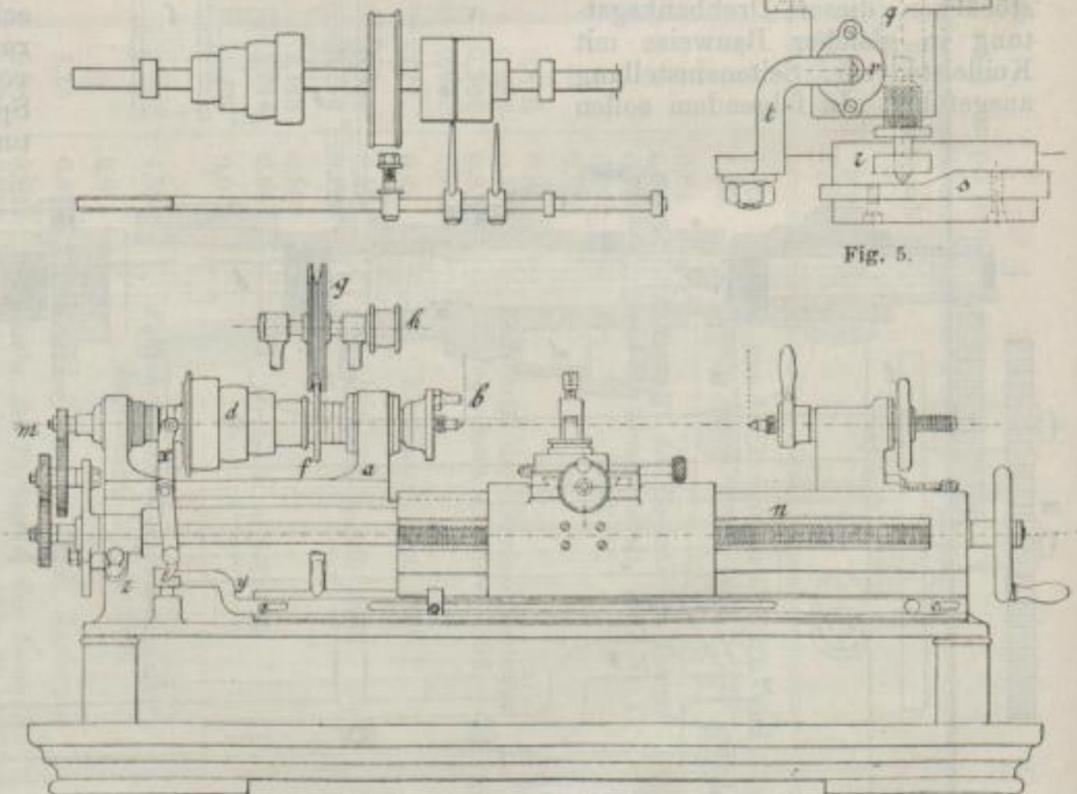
Drehbank für Gewindebohrer, Bolzen und ähnliche Werkzeuge.
